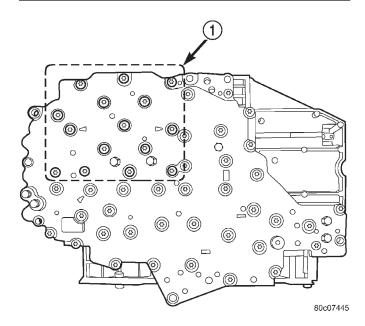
Tornillos del conjunto de TRS/solenoide de la transmisión
